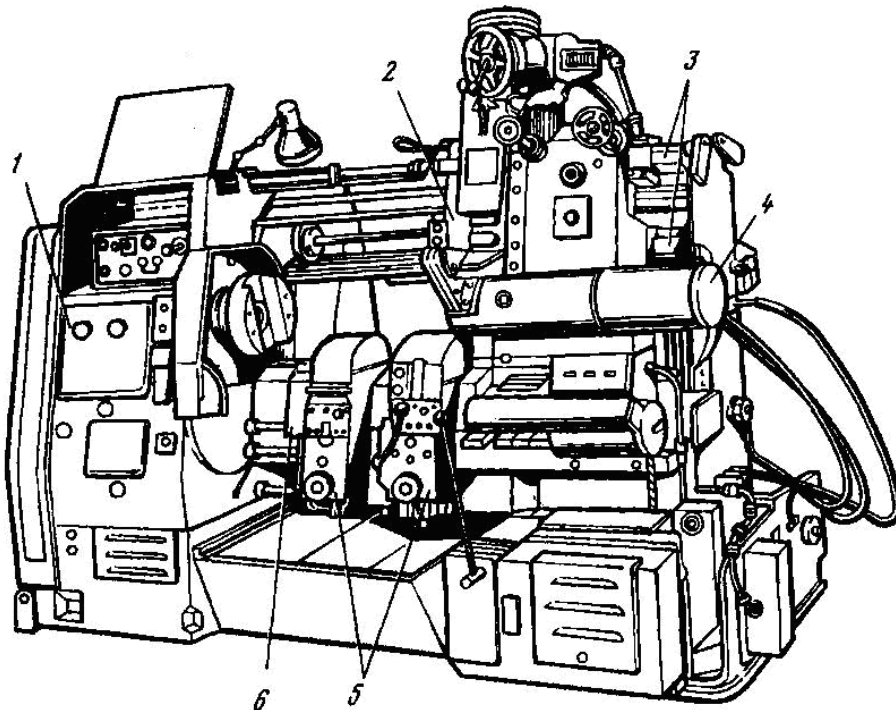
Одношпindelний токарний копіювальний напівавтомат мод. 1722
